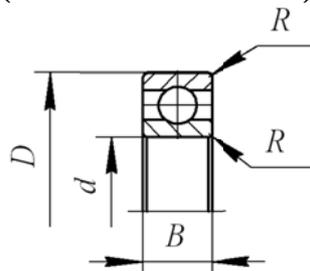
Габаритные размеры шариковых радиальных однорядных подшипников
